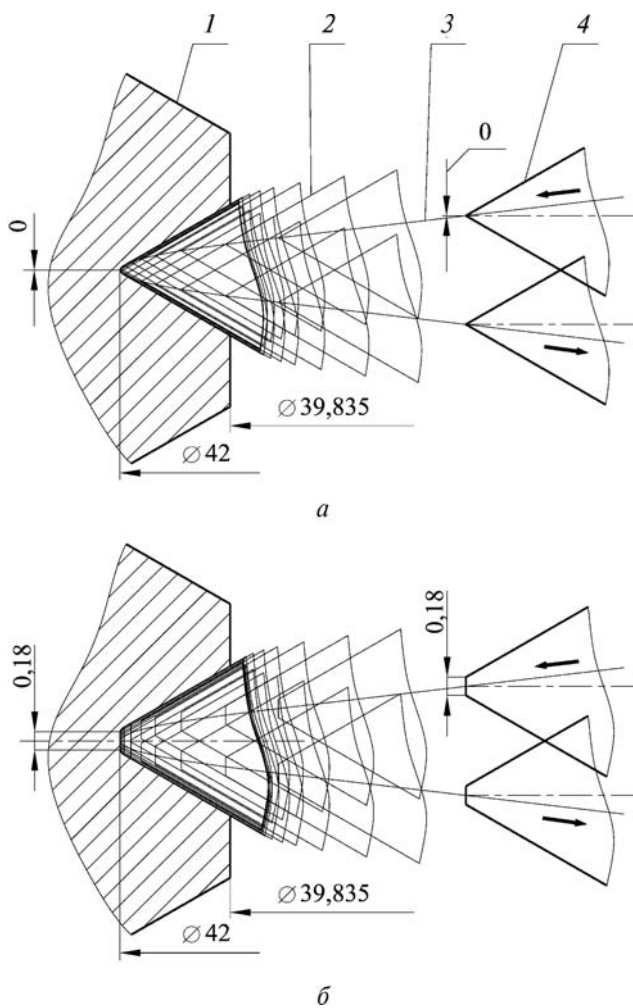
Компьютерное моделирование формирования профиля внутренней резьбы М42×2 зубом резьбообразующей части сверло-резьбофрезы ($d = 36$ мм) с шириной вершины; а — $a = 0$ мм; б — $a = 0,18$ мм
